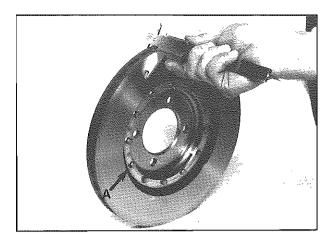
A - Viti di fissaggio - Misurare lo spessore del disco Screws - Measuring disc thickness
